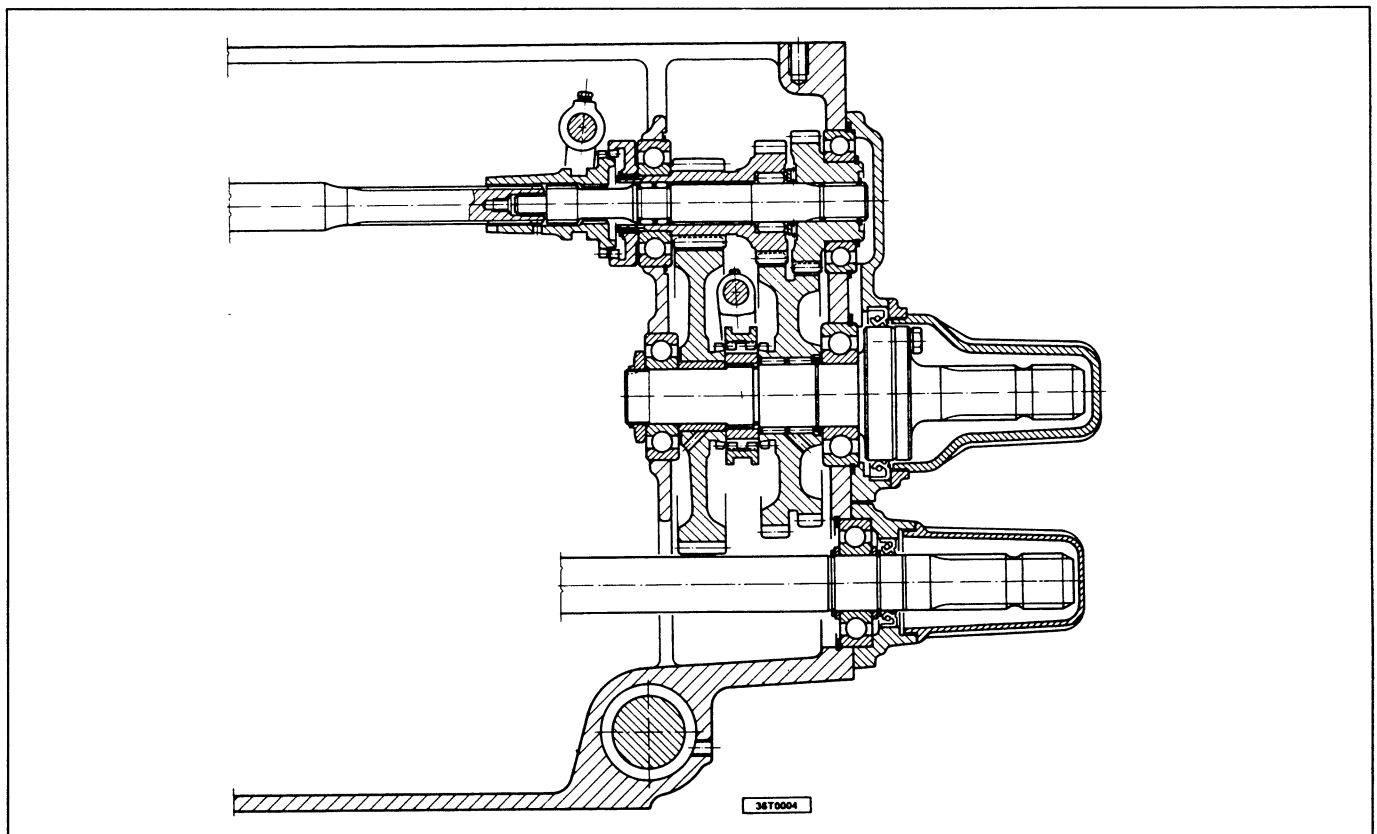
Sección longitudinal del grupo T.D.F. trasera y sincronizada para Explorer II.
